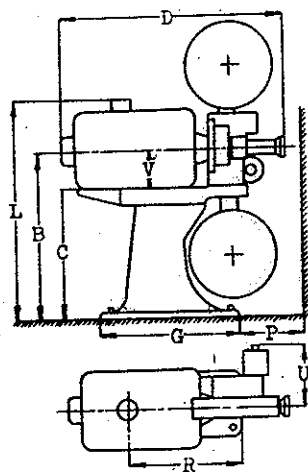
Univerzální 70/35 mm promítač stroj MEOPTA UM 7035
